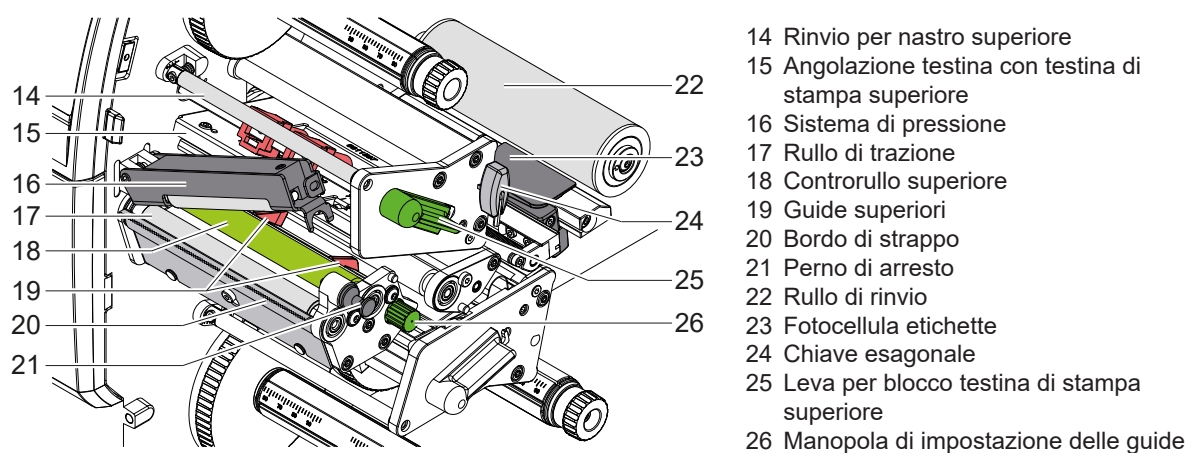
Meccanica di stampa - Gruppo di stampa superiore
